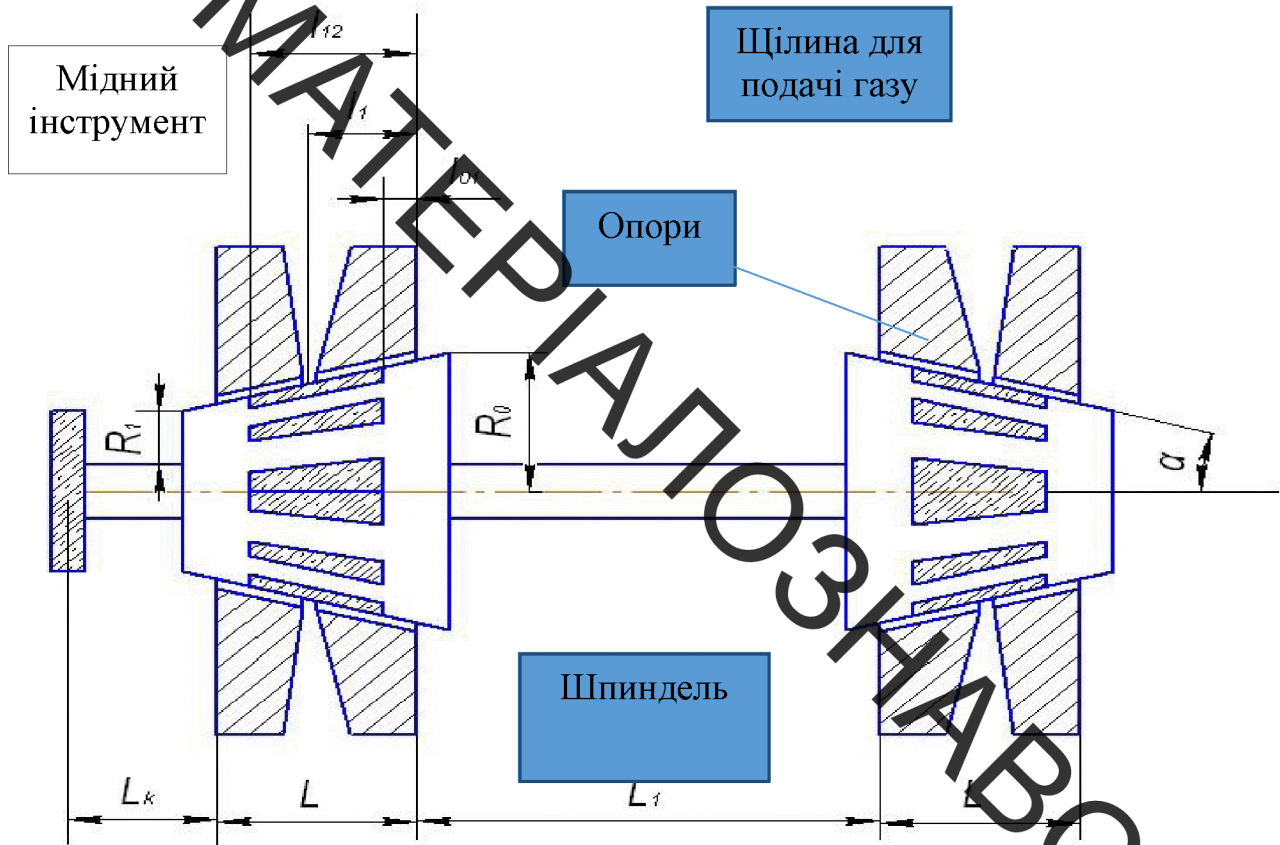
Схема конструкції пристрою на газових опорах для швидкої фрикційної обробки робочих колі насосів земснарядів з частотою обертання 10 000 об/хв
